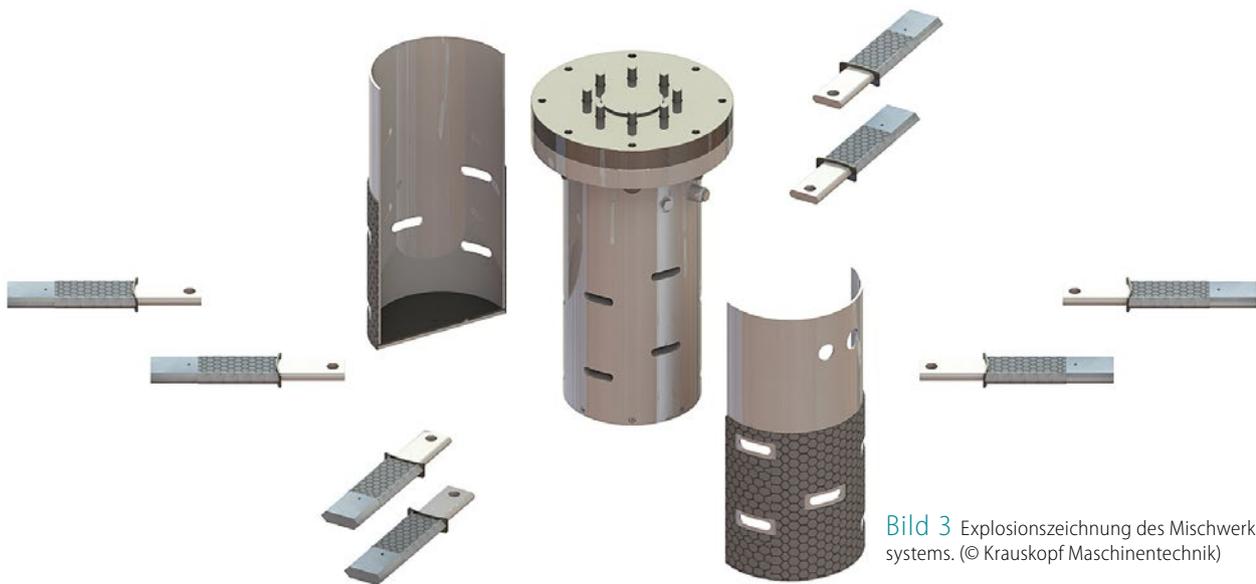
Explosionszeichnung des Mischwerkzeugsystems. (© Krauskopf Maschinentechnik)
